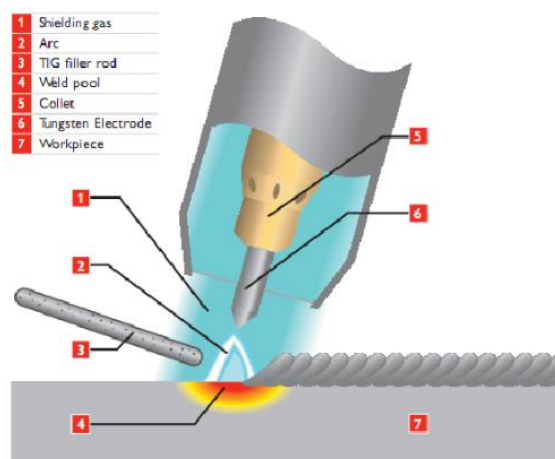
Схема выполнения ручной дуговой сварки
